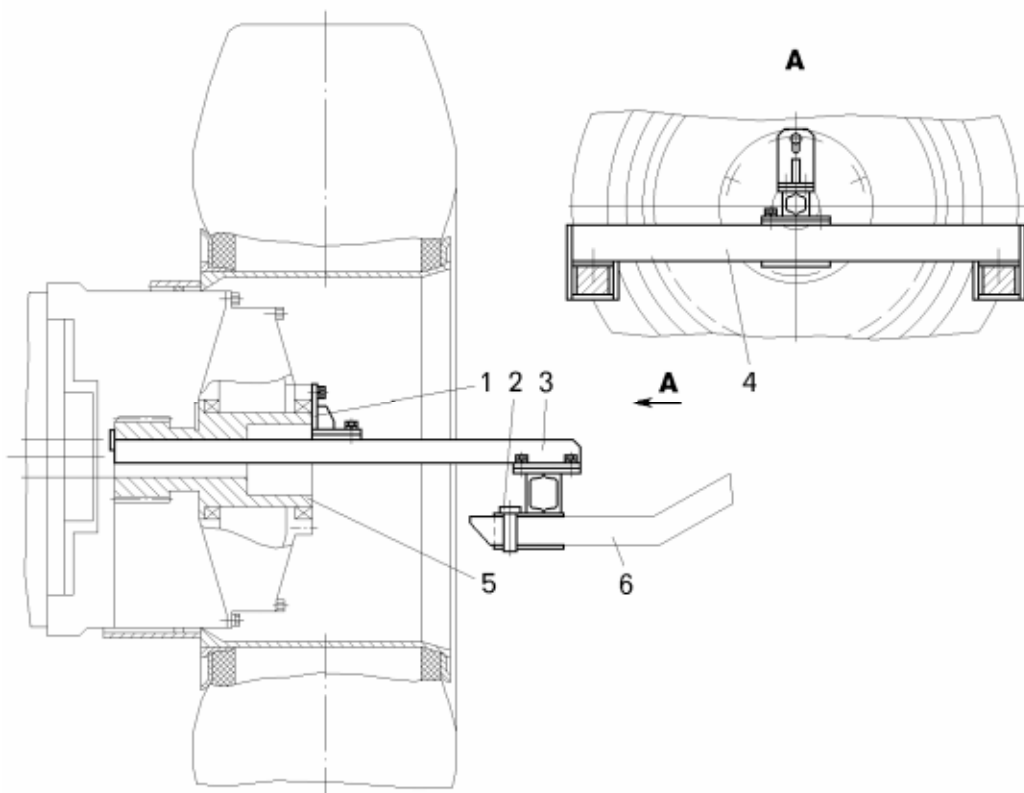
Приспособление 360-008 для снятия и установки водила первого ряда (приспособление используется как навесное оборудование к погрузчику L-34):
